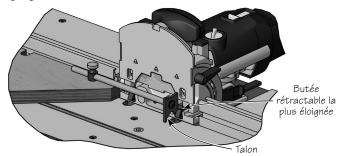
Ajustement de la position inversée du guide coulissant avec la pige de réglage
